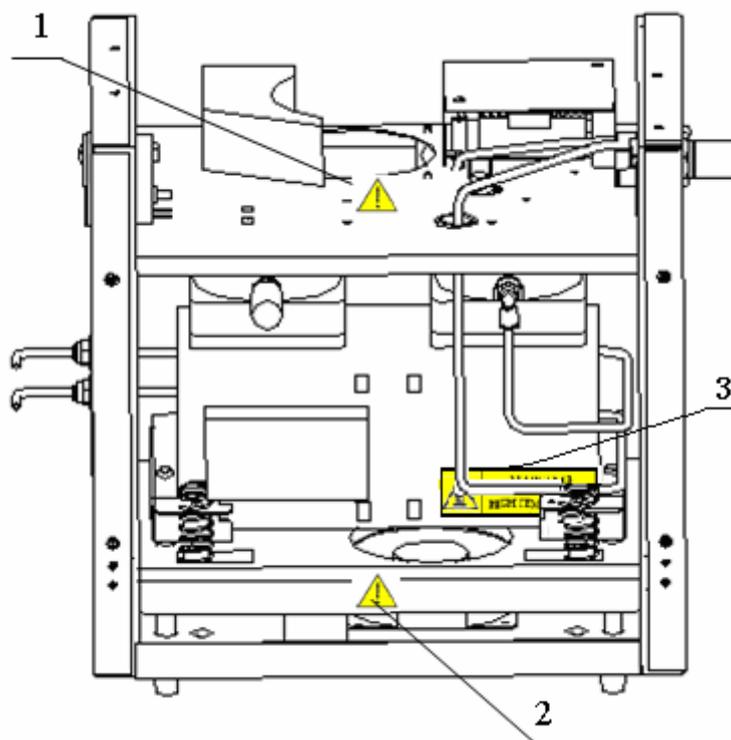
Внутренняя часть пневматического блока, вид слева (крышка снята)
